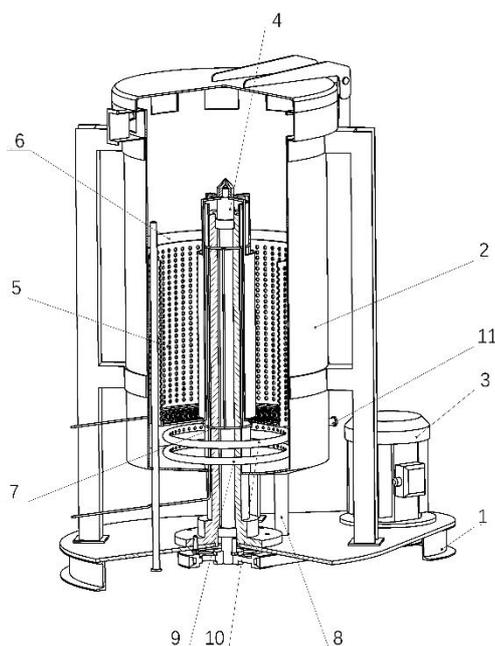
Установка для осуществления ЭГУ: 1 - основание; 2 - ёмкость реактора; 3 - электродвигатель; 4 - вертикальный вал; 5 - перфорированный съемный контейнер; 6 - внешний отрицательный электрод; 7 - центральные положительные электроды; 8 - сливной патрубок; 9, 10, 11 - патрубки подачи технологических сред
